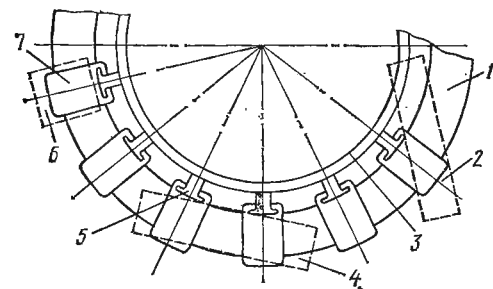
Расположение деталей при подготовке к стяжке и прессовке обмоток:
